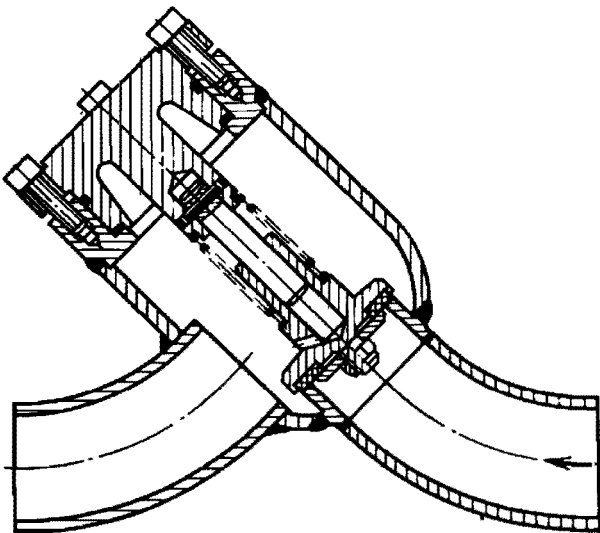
Обратный клапан в сварном корпусе с наклонным седлом (VEB MAW Armaturenwerk, ГДР, Пренцлау)
